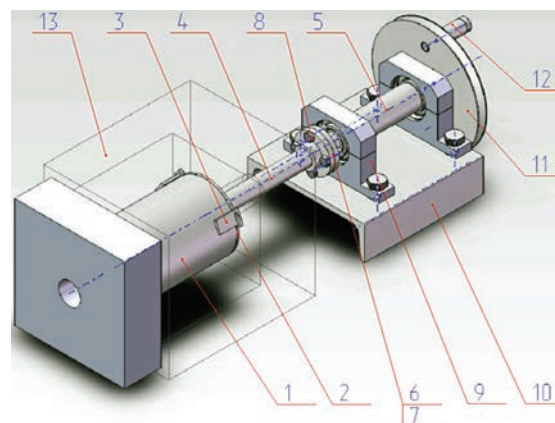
Схема ротационной лабораторной установки: 1 – металлический стакан; 2 – крышка стакана; 3 – ушко стакана; 4 – трубка; 5 – вращательный вал; 6, 7 – фланцы; 8 – фиксирующий винт; 9 – узел подшипниковый; 10 – станина; 11 – шкив; 12 – ручка; 13 – корпус электрической муфельной печи
